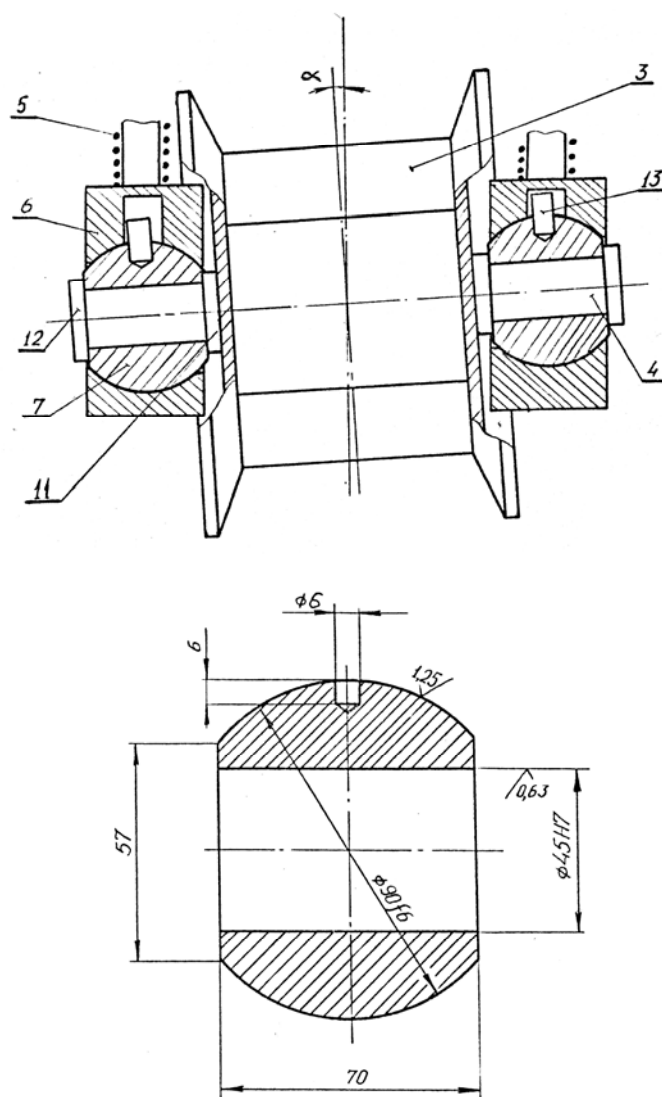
Подшипники оси натяжного барабана с шаровыми вкладышами.
